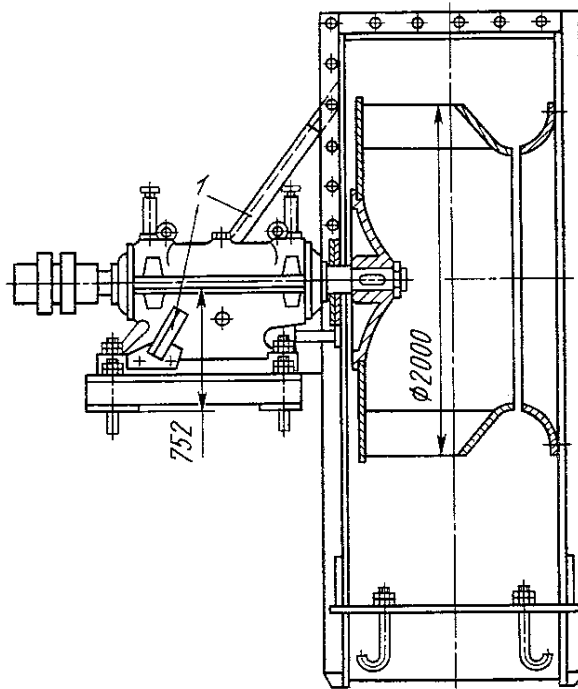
Конструкция корпуса вентилятора, имеющего швеллер жесткости
